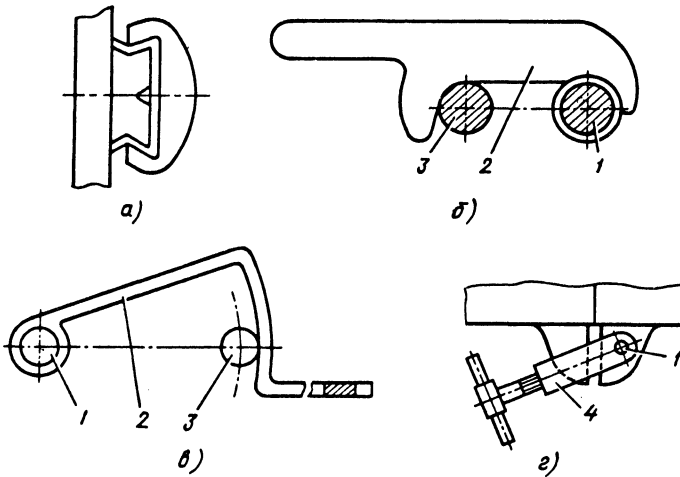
Запорные устройства для скрепления частей кокиля:
